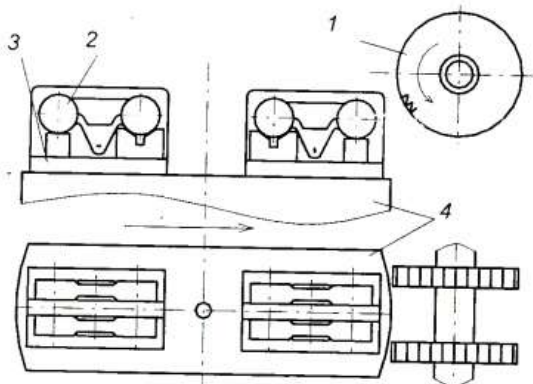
Схема багатомісного фрезерування поверхнь головок
